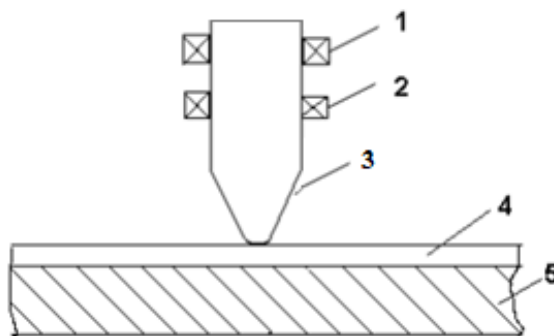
Условная схема индукционного толщиномера: 1 – возбуждающая обмотка; 2 – измерительная обмотка; 3 – ферромагнитный сердечник; 4 – немагнитное покрытие; 5 – ферромагнитная основа
